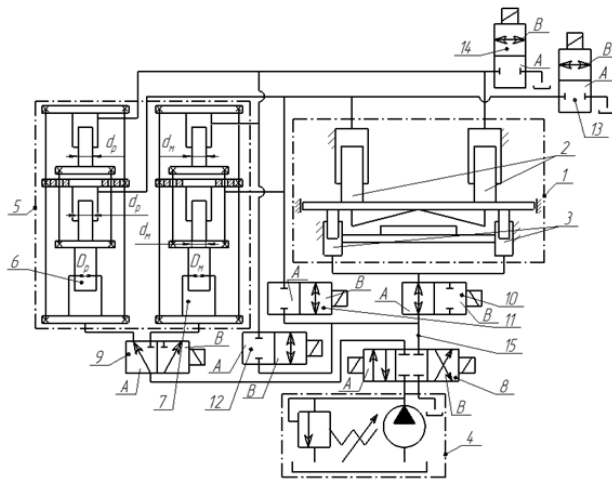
Схема двухцилиндрового двухскоростного редукторно-мультипликаторного привода
